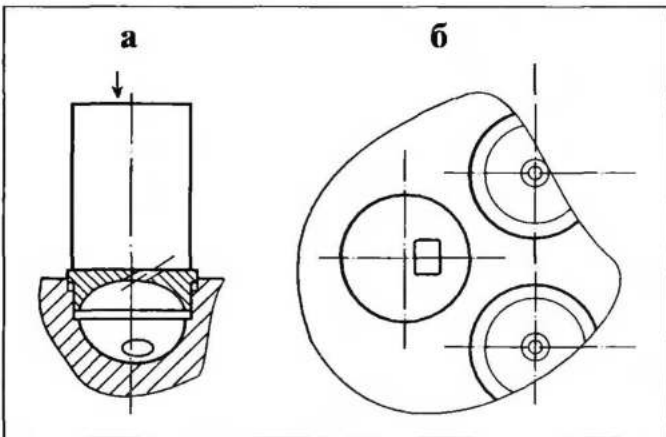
Схема установки вставки (крышки) форкамеры:
